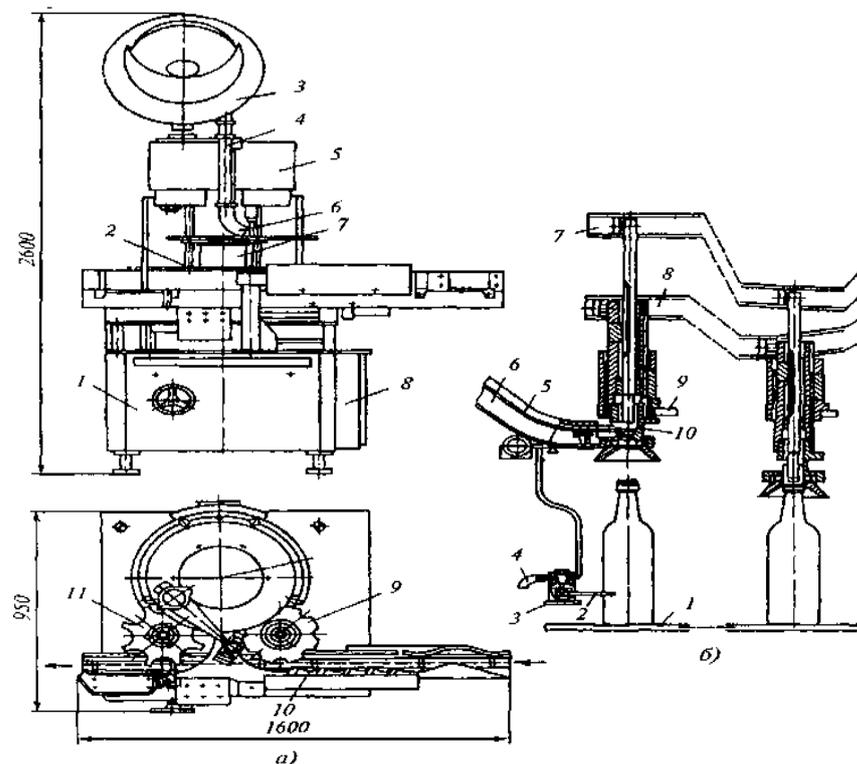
Машина ВУП для закупорювання пляшок:
